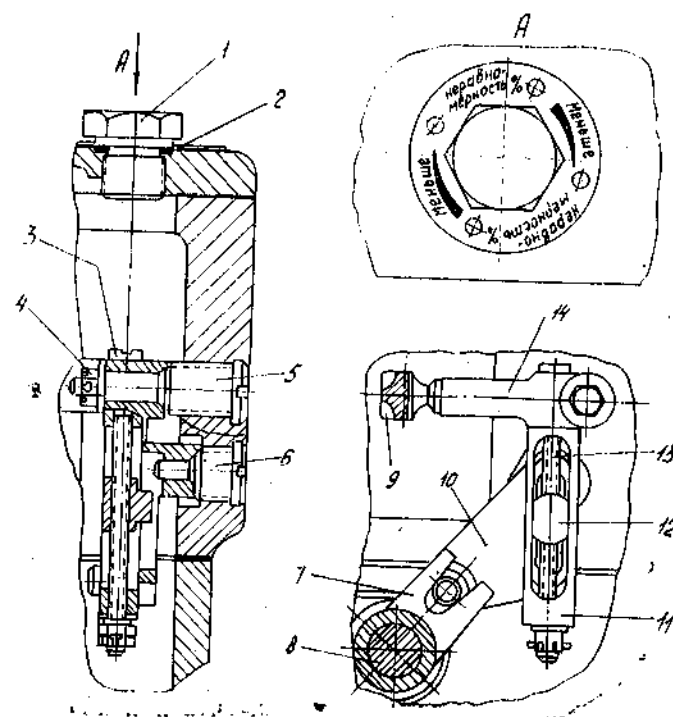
Механизм изменения наклона регуляторной характеристики: 1—пробка; 2—прокладка; 3—головка винта; 4—гайка; 5—ось; 6—рычаг сервомотора; 8—ось рычага сервомотора; 9—суммирующий рычаг; 10—ведущий рычаг; 11—ведомый рычаг; 12—ползун; 13—винт; 14—рычаг
